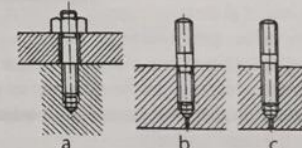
Asamblare cu prezon: a - asamblarea; b, c - variante constructive de prezon (cu și fără degajare).
